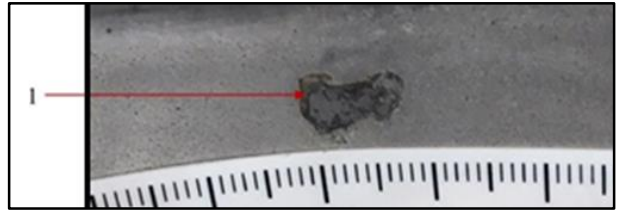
Увеличенный фрагмент основной части пресс-формы станка
